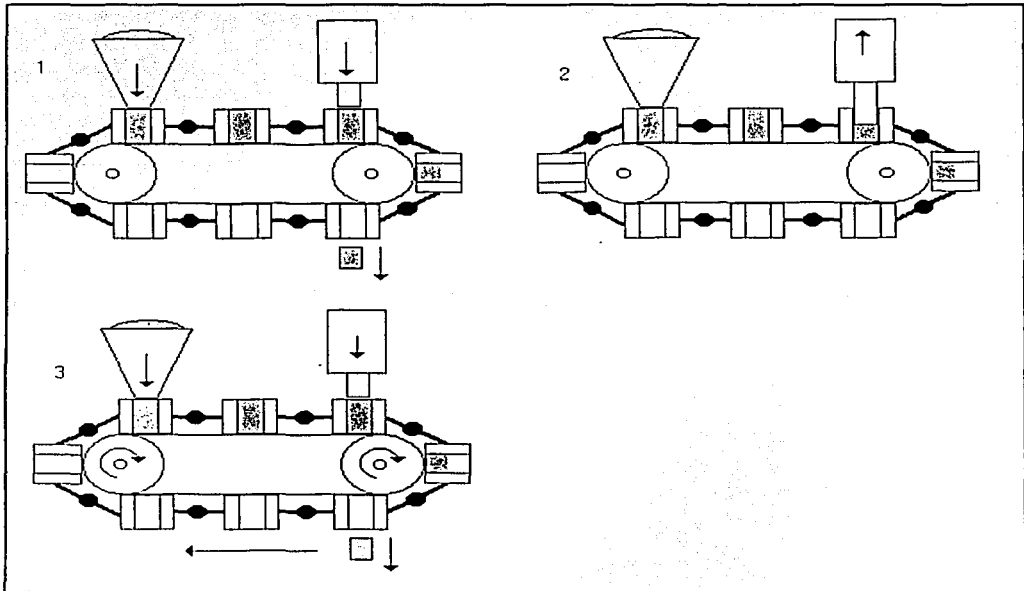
Sistema de conformado por pistón con molde montado en banda.
